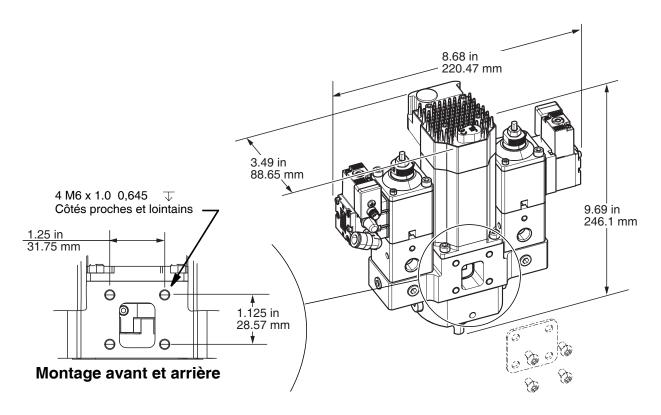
Dimensions de la vanne de mélange dynamique Voltex
